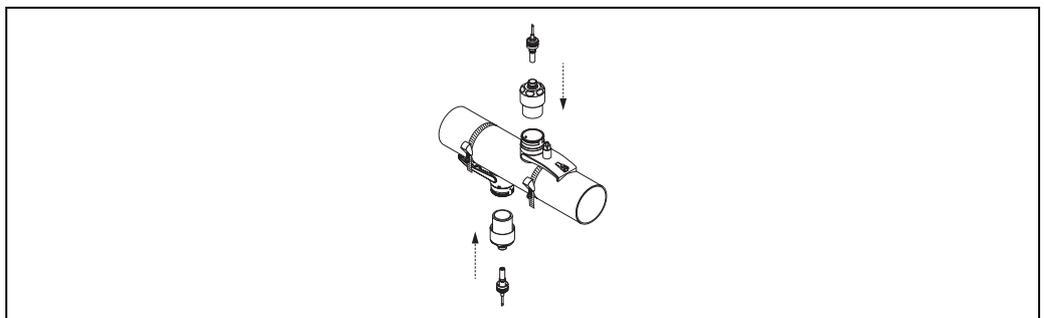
Montaggio del sensore e collegamento del cavo di collegamento
